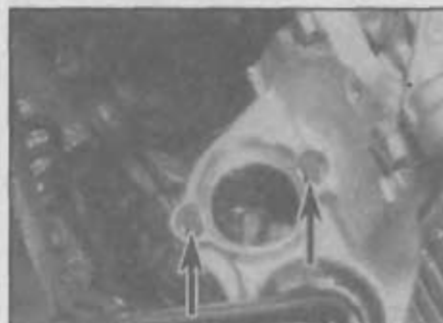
Положение болтов, при которых их головки смещены от наружного кольца подшипника
